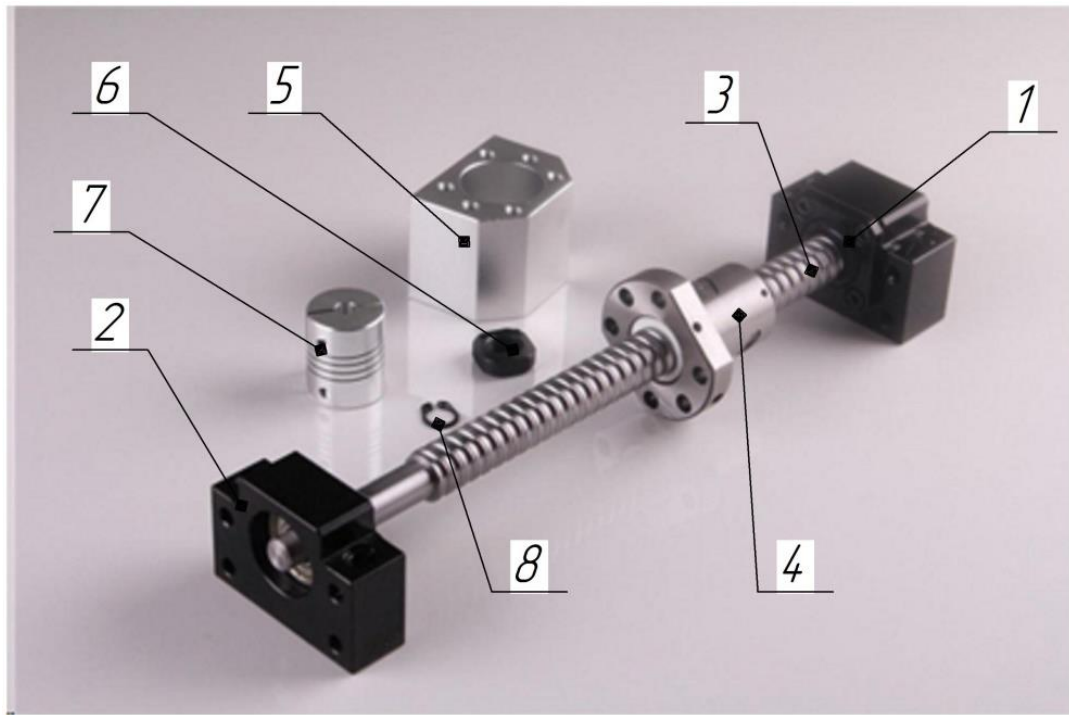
Кулько–гвинтова передача: 1–підшипник; 2–опора гвинта (фланець підшипника); 3–гвинт; 4–гайка; 5–кронштейн для гайки; 6–гайка для фіксації гвинта; 7–муфта для з'єднання з двигуном; 8–стопорне кільце
